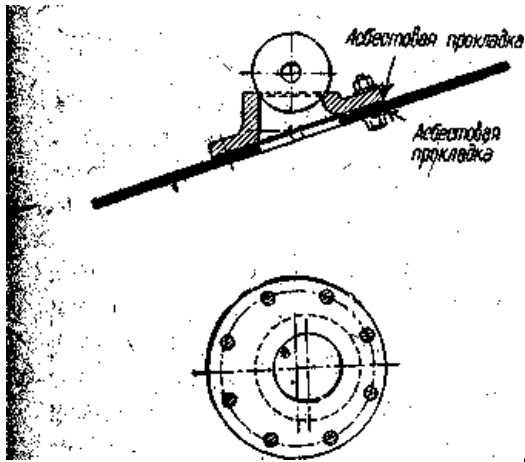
Деталь шуровочного отверстия, закрываемого шаром.
